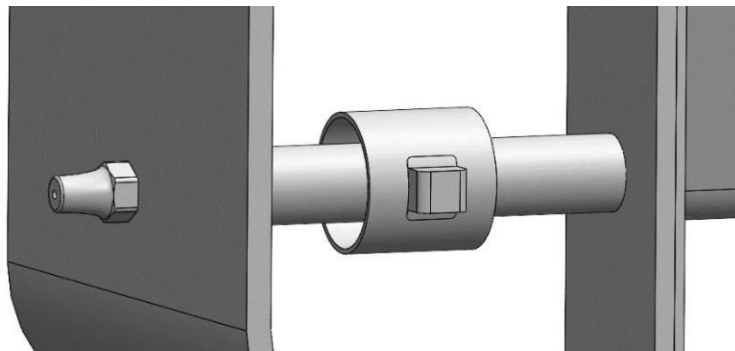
Cabezal extrusor de la máquina recicladora.
